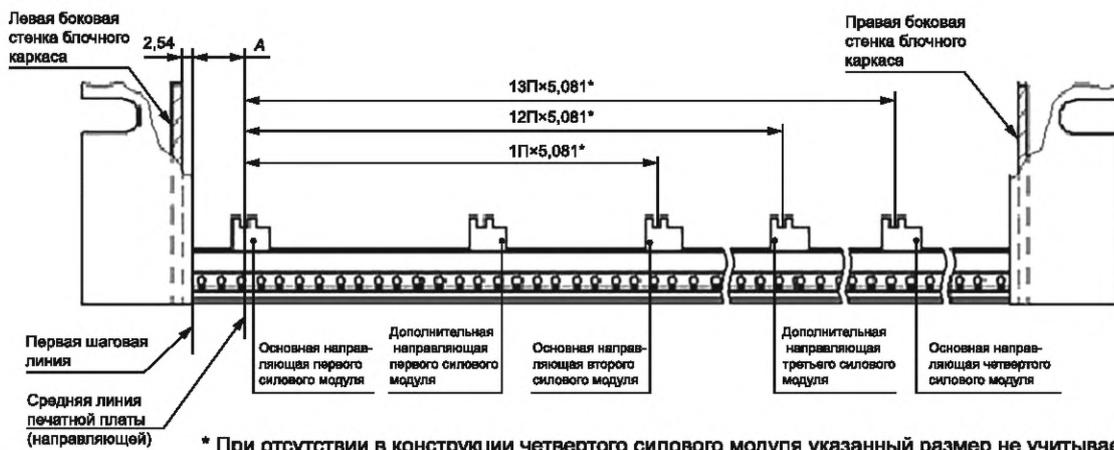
Общий вид расположения нижних направляющих в блочном каркасе
